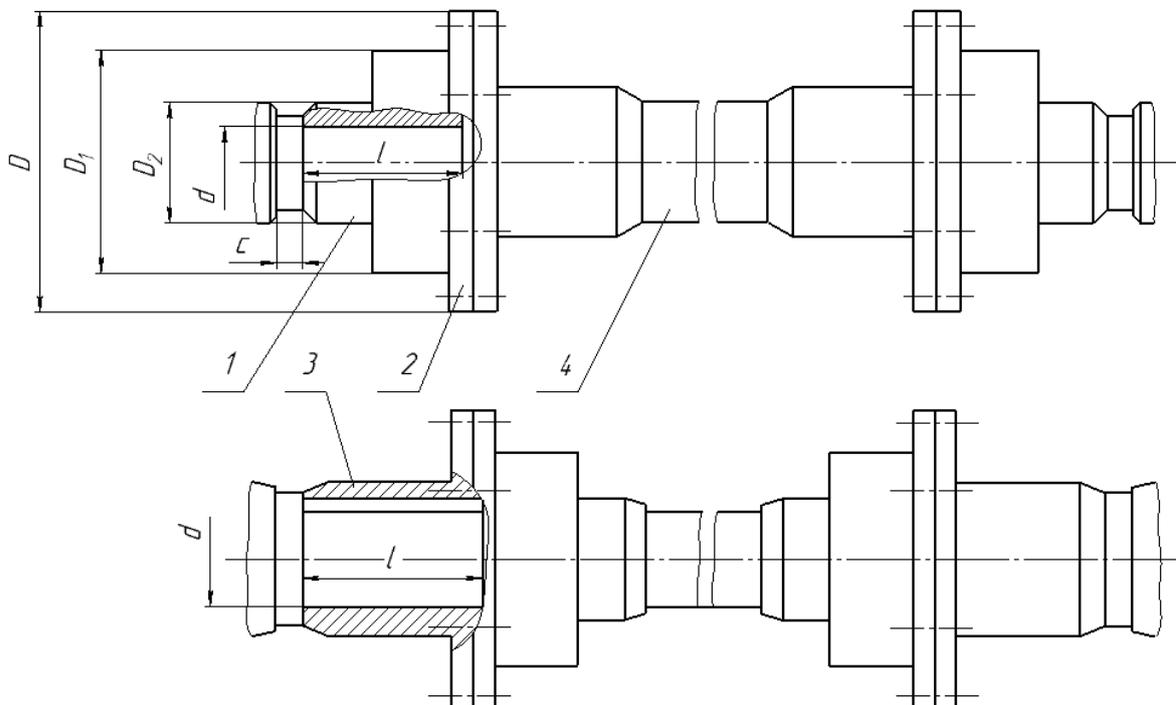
1 – втулка; 2 – обойма; 3 – фланцевая полумуфта; 4 – промежуточный вал
